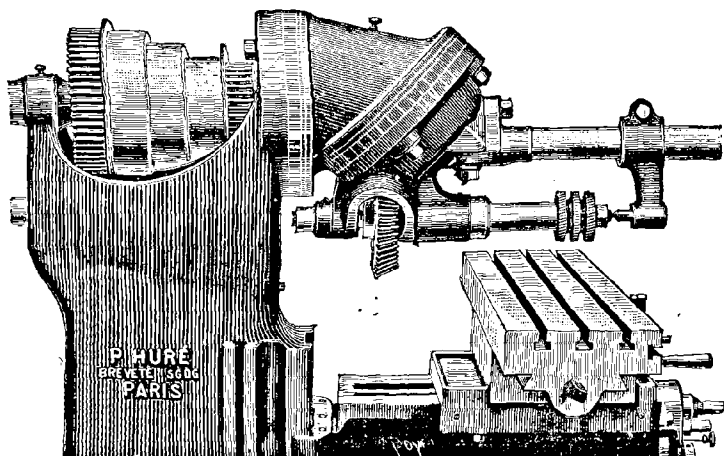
Fraiseuse Huré disposée pour fraiser horizontalement.
